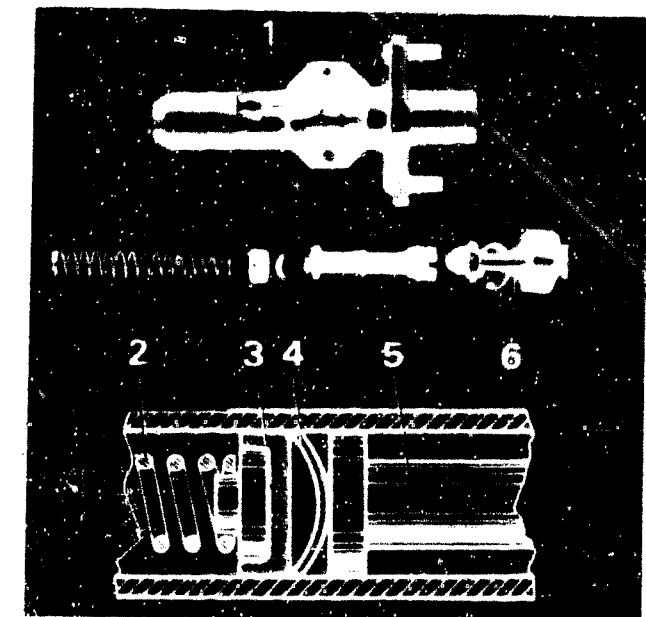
Einzelteile des Betätigungszyinders mit der Einbaulage der Scheibe 4 (unten). 1 Gehäuse – 2 Druckfeder – 3 Manschette – 4 Scheibe – 5 Kolben mit hinterer Dichtung – 6 Kolbenstange mit Anschlägscheibe, Sprengring und Schutzkappe.
